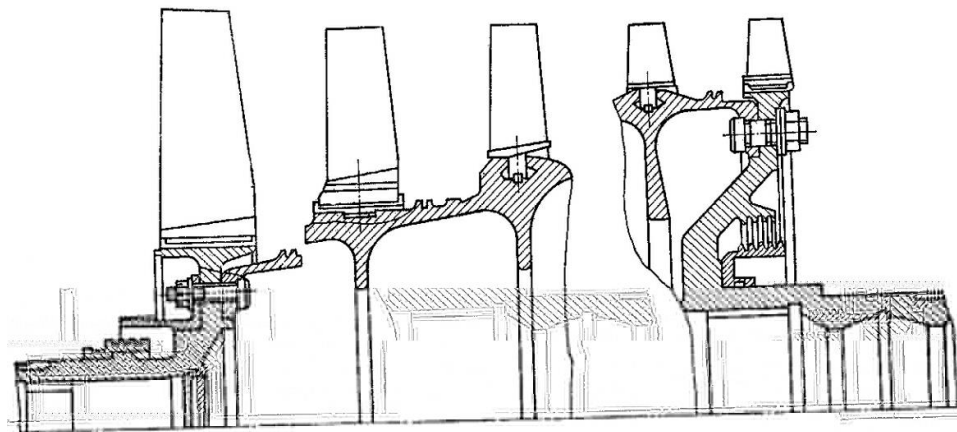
Ротор барабанного типа, изготовленный из титанового сплава с упрочняющими внутренними кольцевыми ребрами
